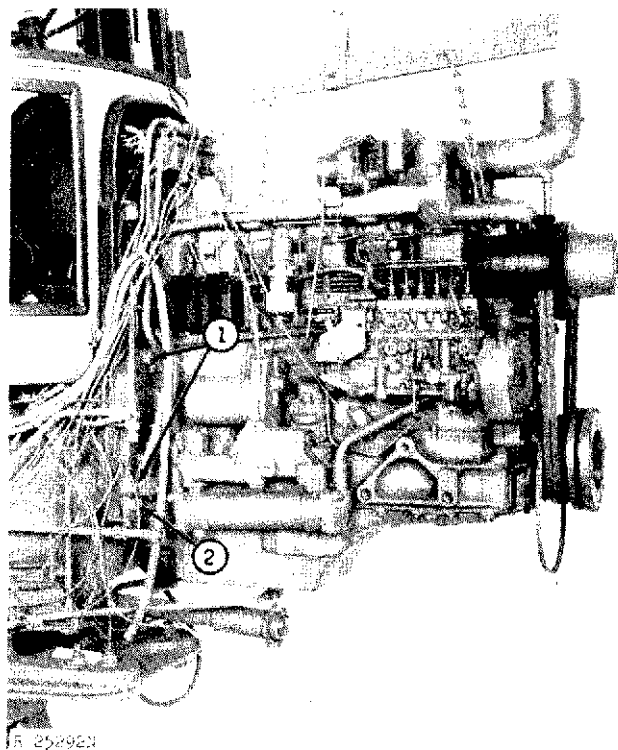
Estructura del Motor Instalado (Se Muestra el 8630)
